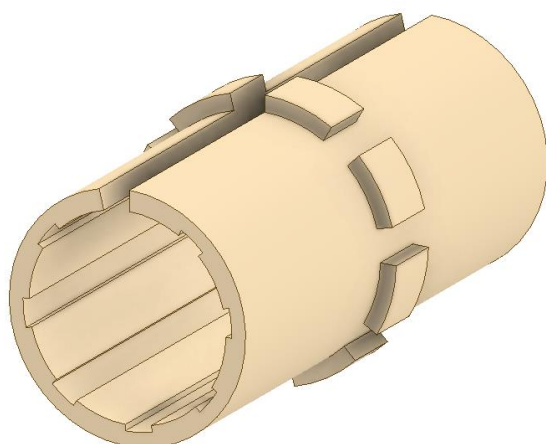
Lineární kluzné vedení bočního přítlačného mechanismu
